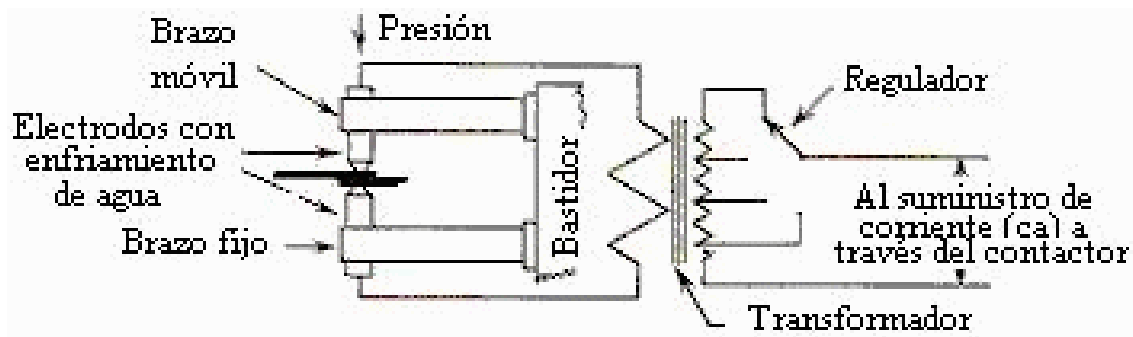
Diagrama de una maquina soldada por puntos.
